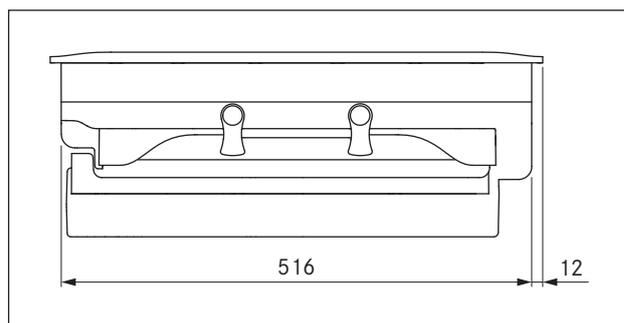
Dimensions PKAS, PKASAB vue de côté
